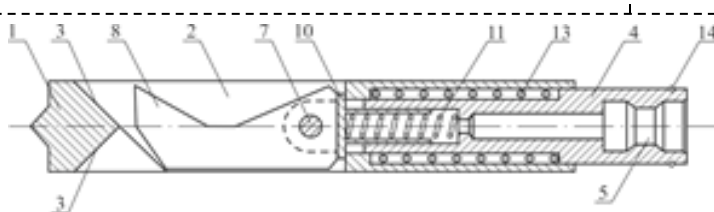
Схема щелеобразователя разработки ФГБУ Институт угля СО РАН: 1 – стакан; 2 – продольное окно; 3 – перекрестные оппозитные направляющие уклоны; 4 – толкатель; 5 – резьбовое отверстие; 6 – проушины; 7 – ось; 8 – режущий орган; 9 – торцовая часть режущего органа; 10 – направляющая втулка; 11 – пружина; 12 – отверстие; 13 – пружина возврата; 14 – упорное кольцо
